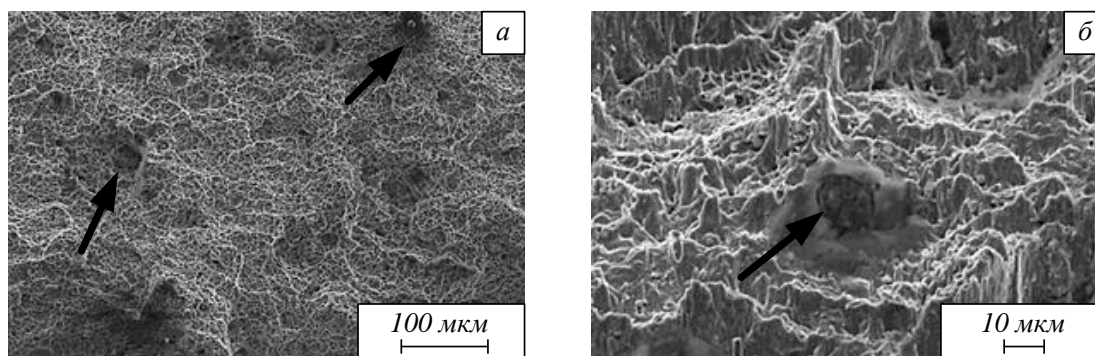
Поверхность вязкого излома металла сварного шва образца 2 (стрелками указаны неметаллические включения)
